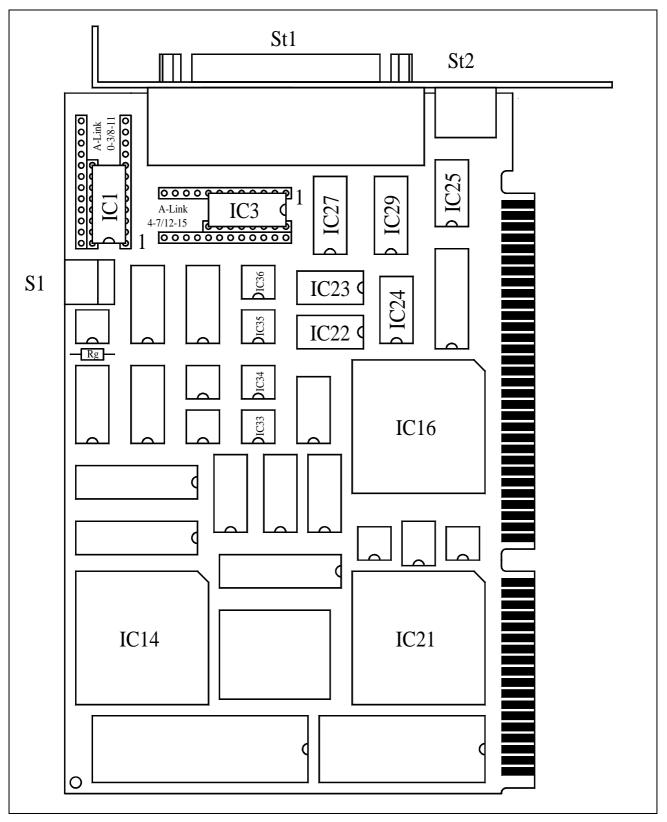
Lageplan der Multi-LAB/2i und /2h, Revision B
